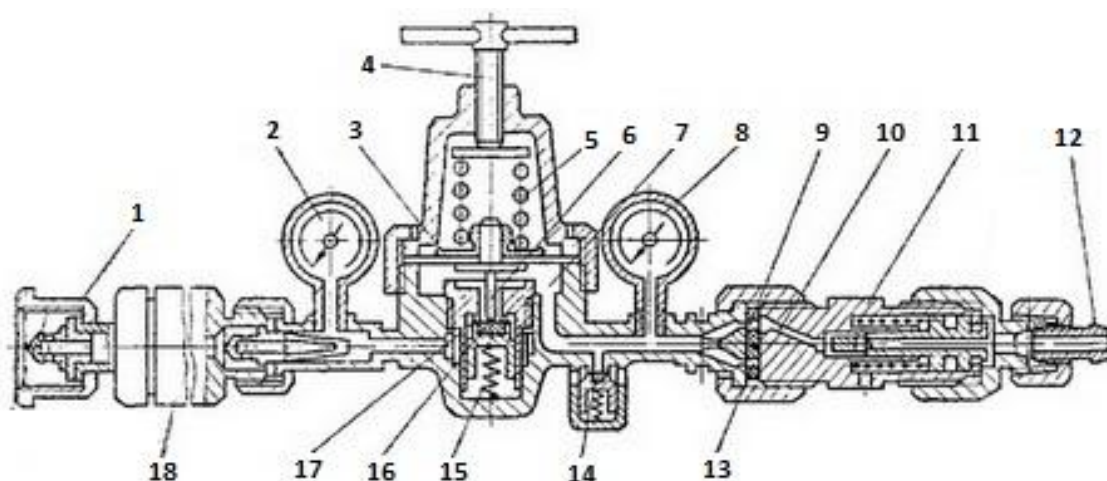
Схема газового редуктора У-30 для углекислого газа:
